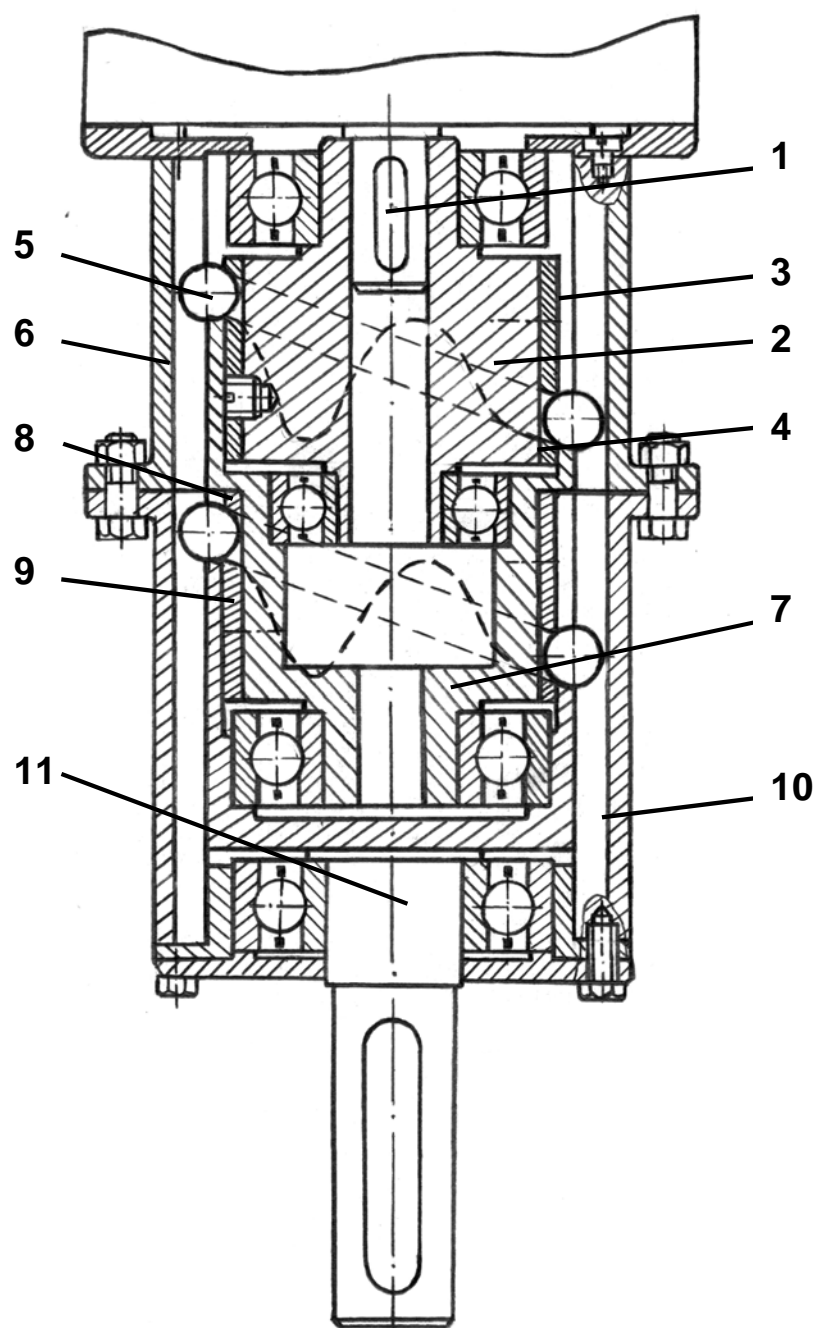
Схема планетарного двухступенчатого шарикового мотор-редуктора
